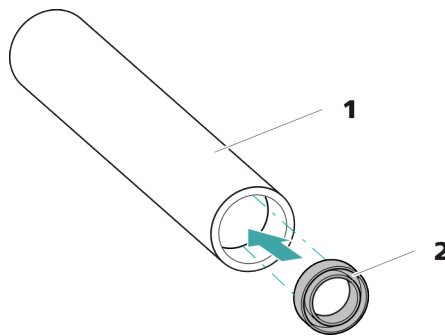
Kolbendichtung in Werkzeug einsetzen
